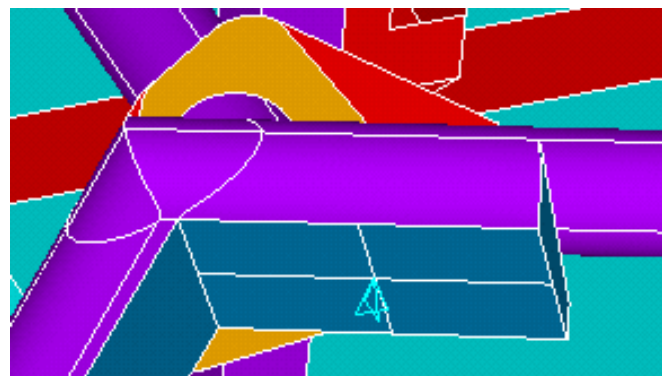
DETALLE RESTRICCIÓN VERTICAL.
